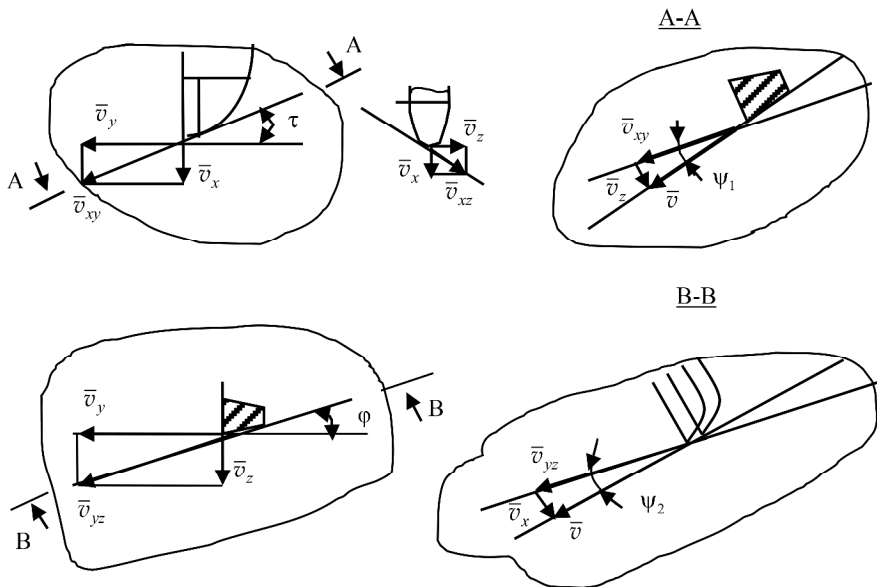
Кинематические углы ψ_1 , ψ_2 вектора абсолютной скорости движения резца для боковой и задней поверхностей инструмента
